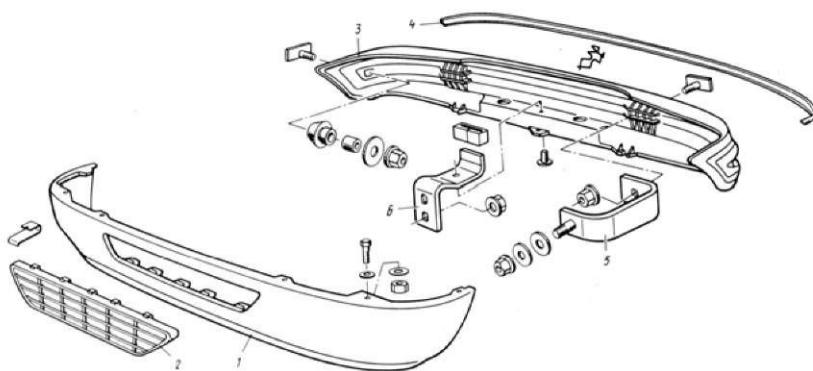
Щитки из композиционных материалов автомобиля: 1 -передний щиток; 2-решетка; 3- задний щиток; 4- декоративная накладка; 5- боковое крепление щитка; 6 - центральное крепление щитка
